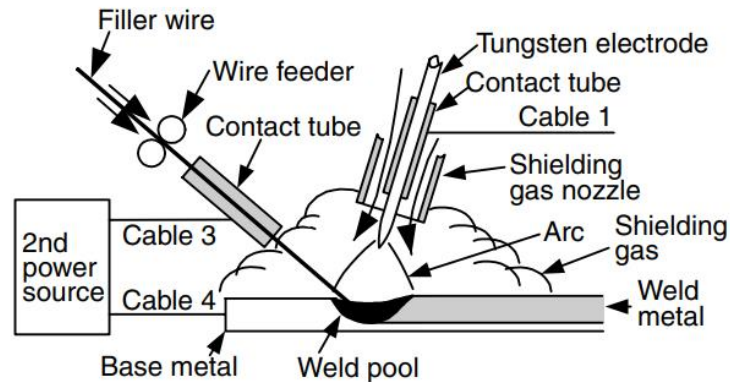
Esquema del proceso de soldadura GTAW [15].
